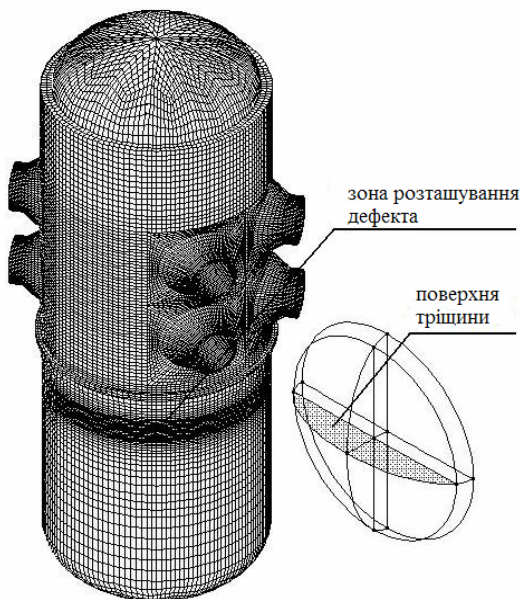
Розрахункова модель корпусу реактора ВВЕР-1000
